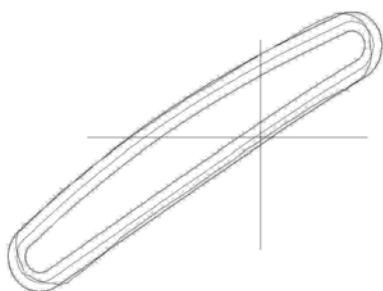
Профилограмма поперечного сечения лопатки широкохордного моноколеса после чистового фрезерования
